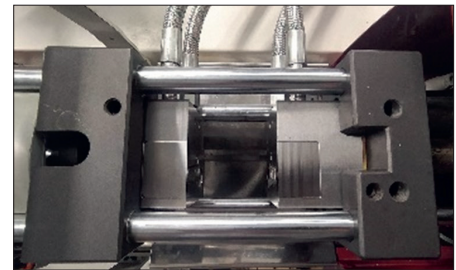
Komplett montiertes Werkzeug auf Spritzgiessmaschine.
